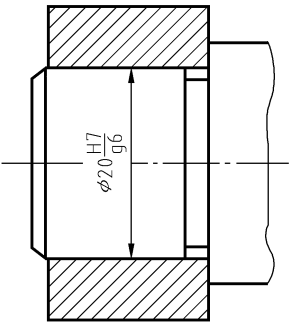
装配图中尺寸公差标注的通用形式
